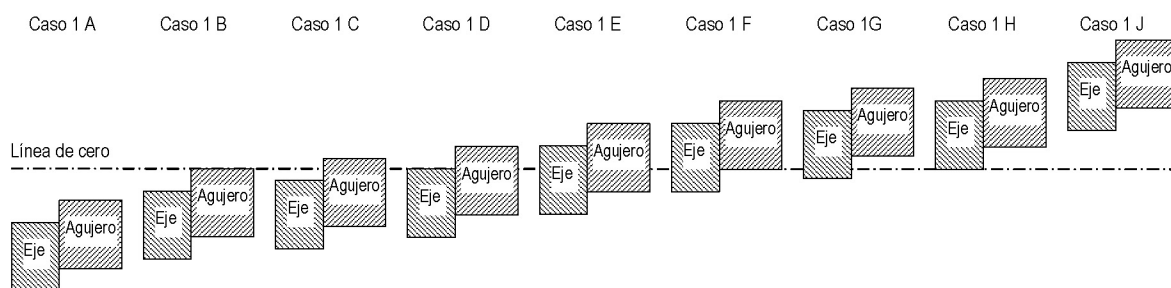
Posiciones relativas de la línea de cero para ajuste indeterminado con tolerancia del eje sobresaliendo por debajo de la tolerancia del agujero
